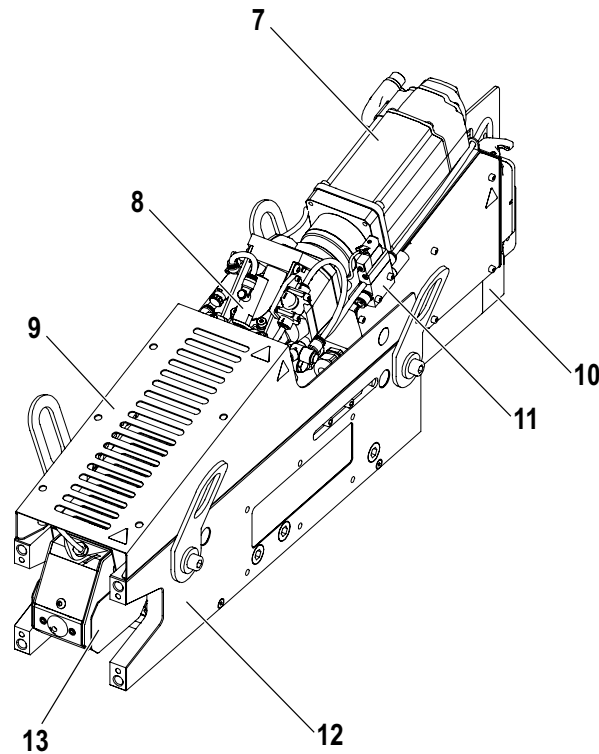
Componentes de la unidad de inyección (parte frontal)
